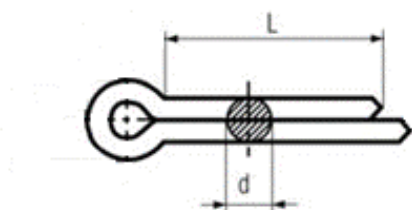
Pasador para las fijaciones de las piezas de conexión.
